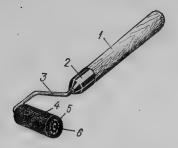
1 — ручка; 2 — колпачок: 3 — кронштейн; 4 — валик; 5 — корпус; 6 — ось
